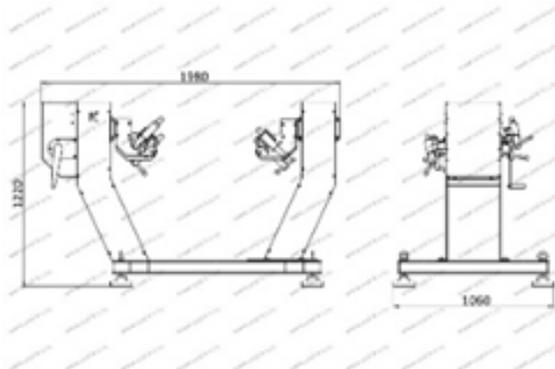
Стенд-кантователь для сборки и разборки двигателя
